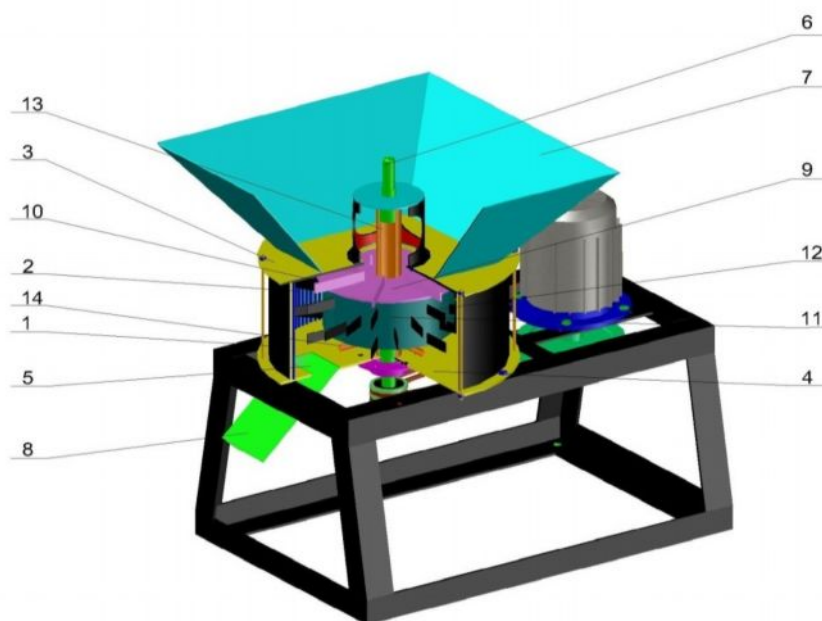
Центробежно-ударный смеситель-активатор [129]:
